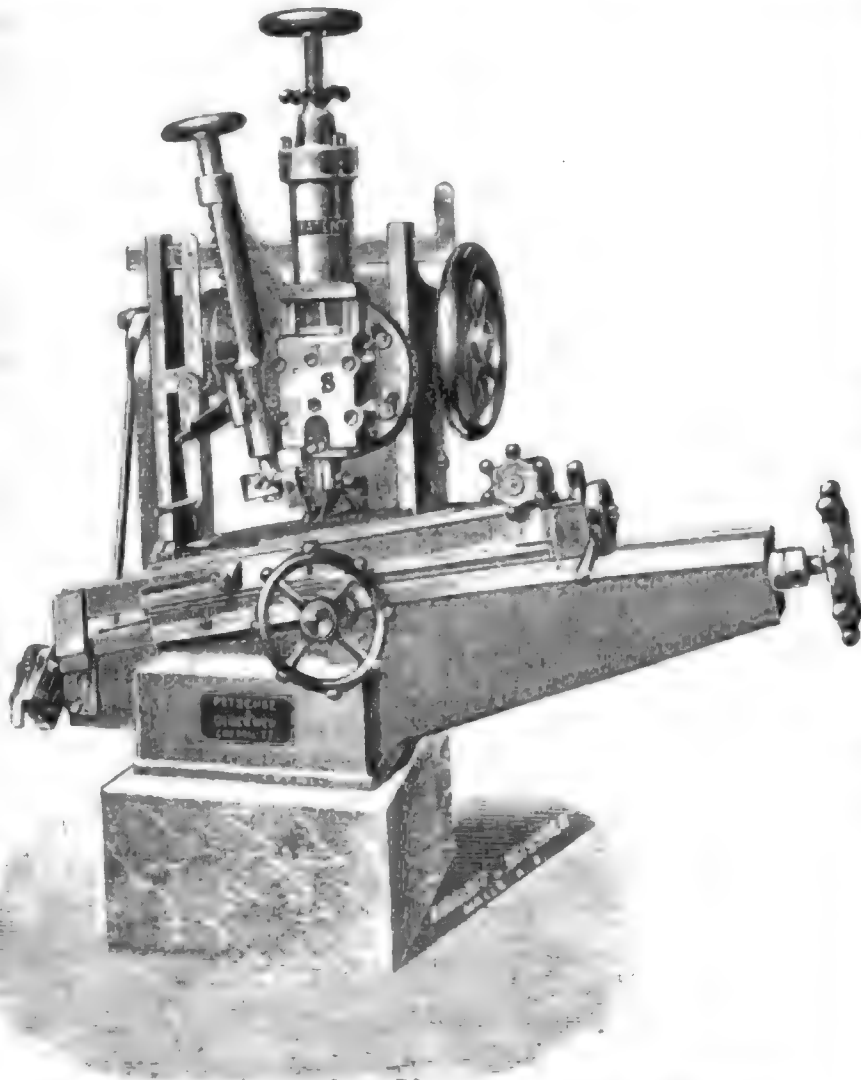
Feilenhausmaschine mit verstellbarem Kopf und gewölbter Bahn.
